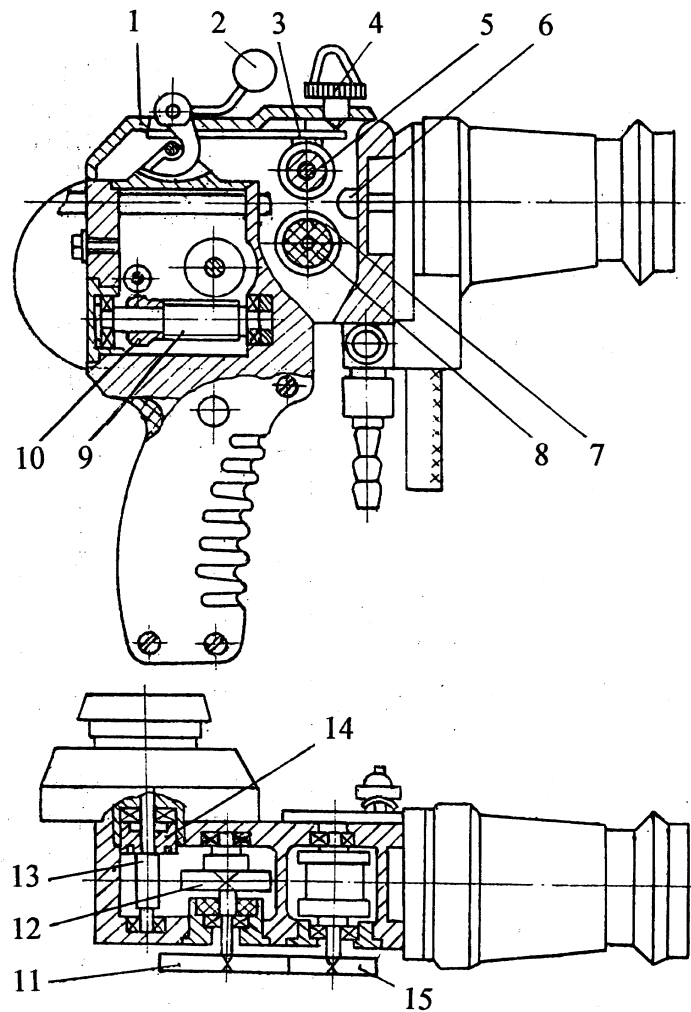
Серійний електродуговий розпилювач типу ЭМ-14М: 1 – кришка; 2 – рукоятка; 3 – пружина; 4 – гвинт притискний; 5 – ролики притискні; 6 – болт спеціальний; 7 – ролики подавальні; 8 – втулки ізоляційні; 9, 13 – черв'яки; 10, 12 – колеса черв'ячні; 11, 15 – шестірні змінні; 14 – ущільнення
